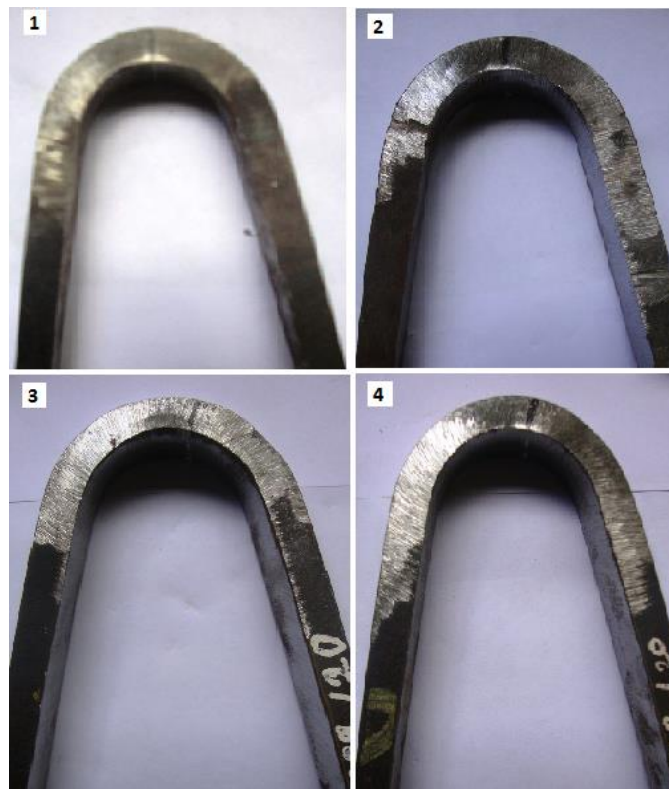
Ensayos de doblado lateral, acero ASTM A36, 24 milímetros. Vista frontal.
